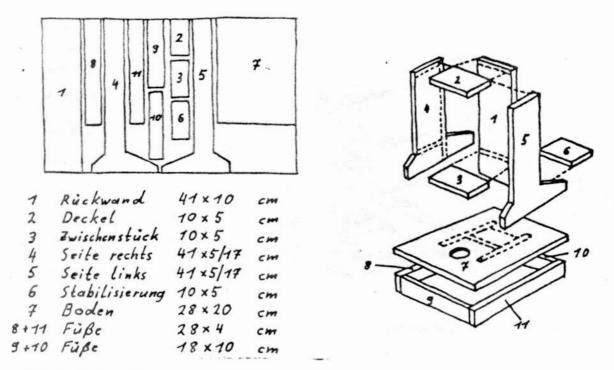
Aussäge-Skizze und Explosionszeichnung des Turmes
